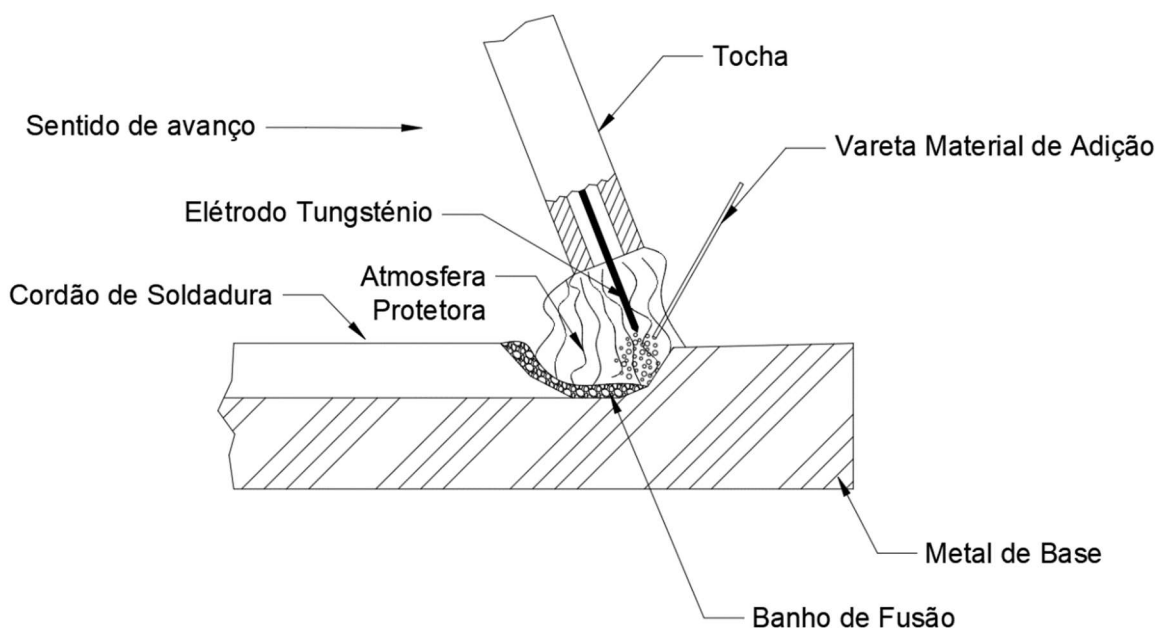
Ilustração esquemática do processo de soldadura TIG.
